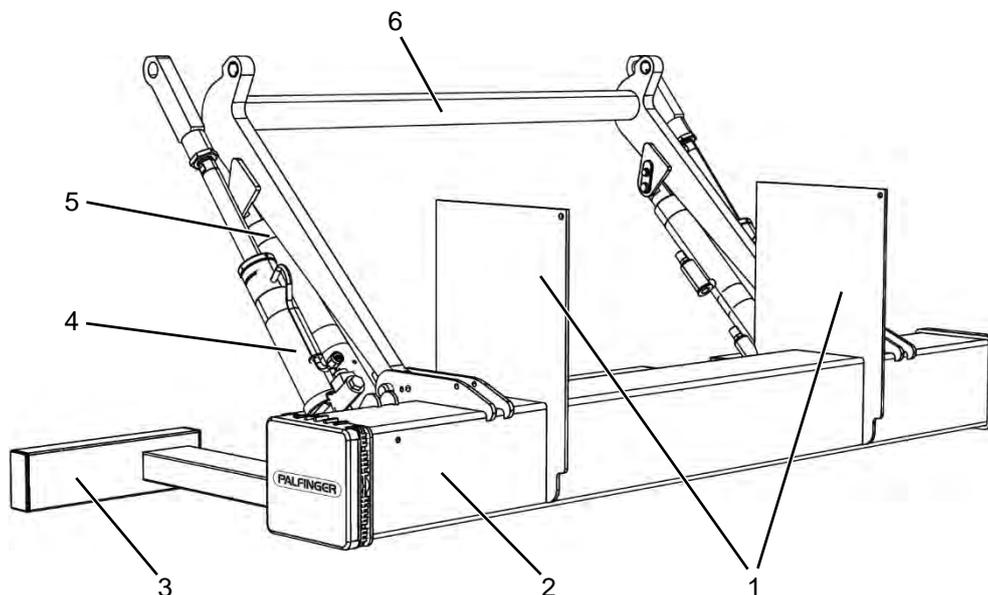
Подъемно-погрузочная платформа с приварными консолями и вставным агрегатом
